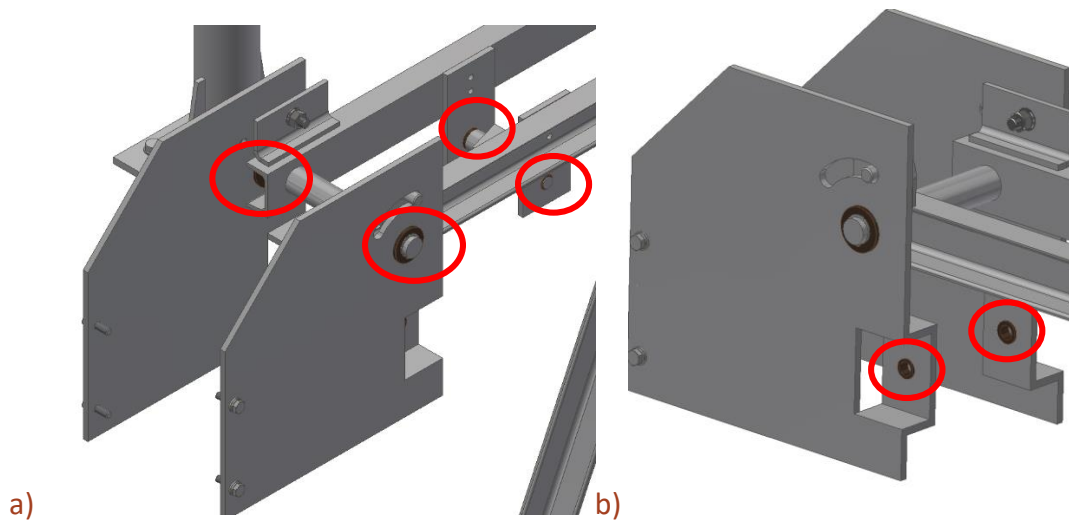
Zonas de inspeção de desgaste nos braços da estrutura e caixas guia: vista frontal a) e vista traseira b)
